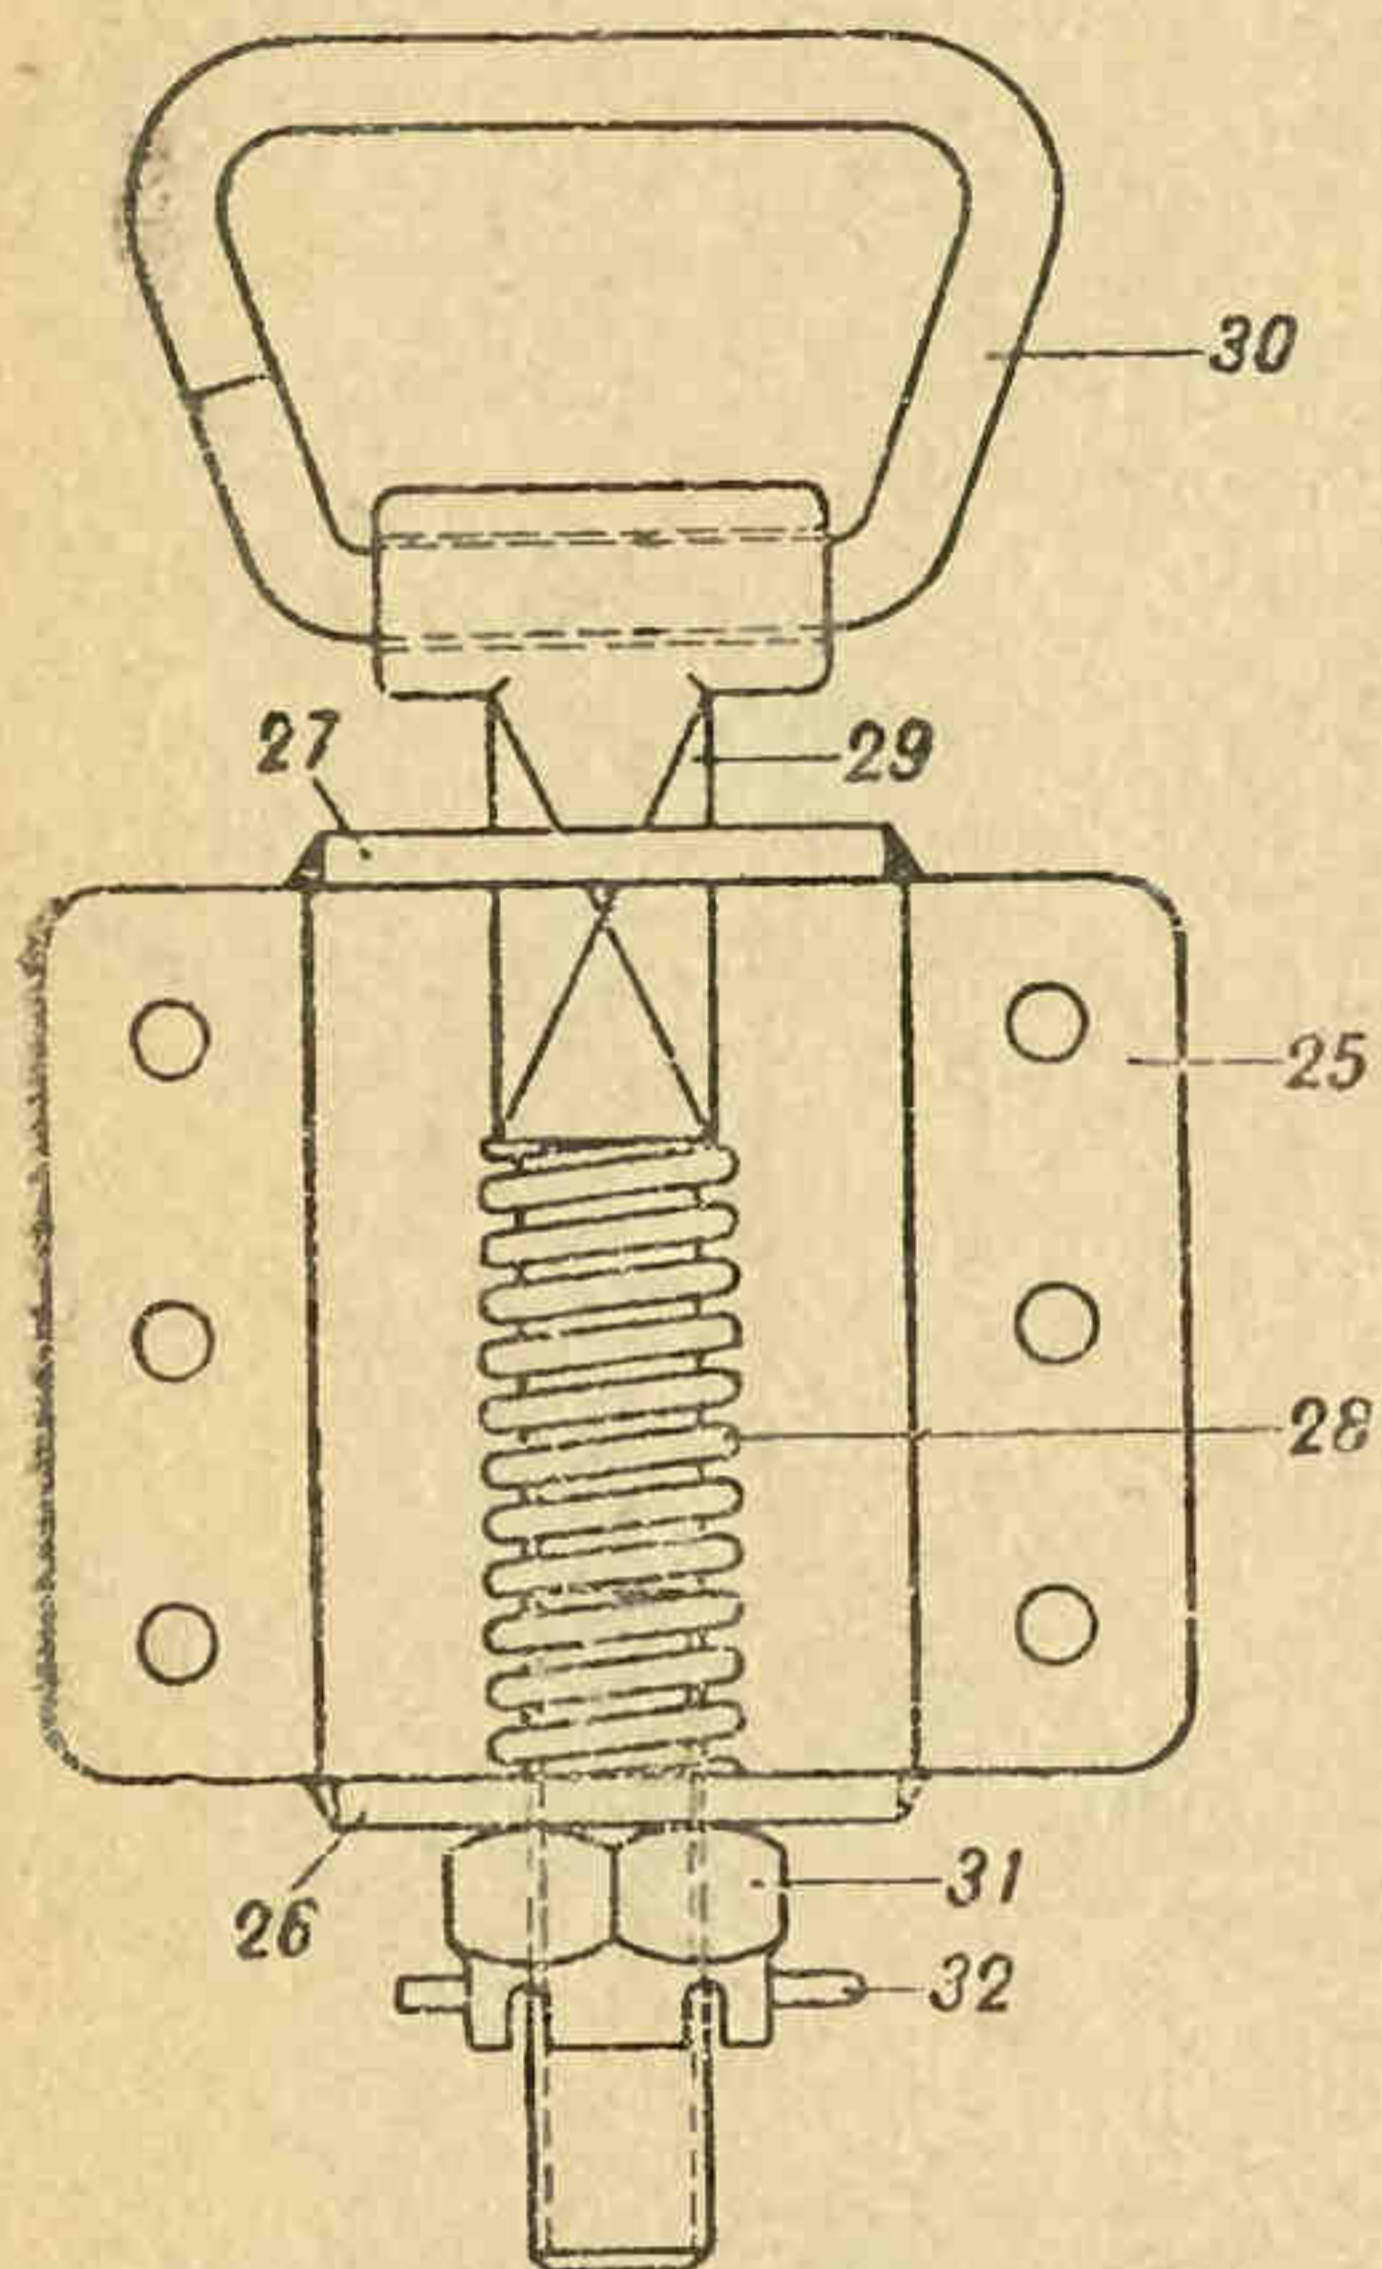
Державка прижима: 25 — коробка державки (02-31); 26 — дно коробки (02-33); 27 — крышка (02-32); 28 — пружина (02-36); 29 — болт (02-34); 30 — петля (02-35); 31 — гайка (02-37); 32 — шплинт (02-38)
